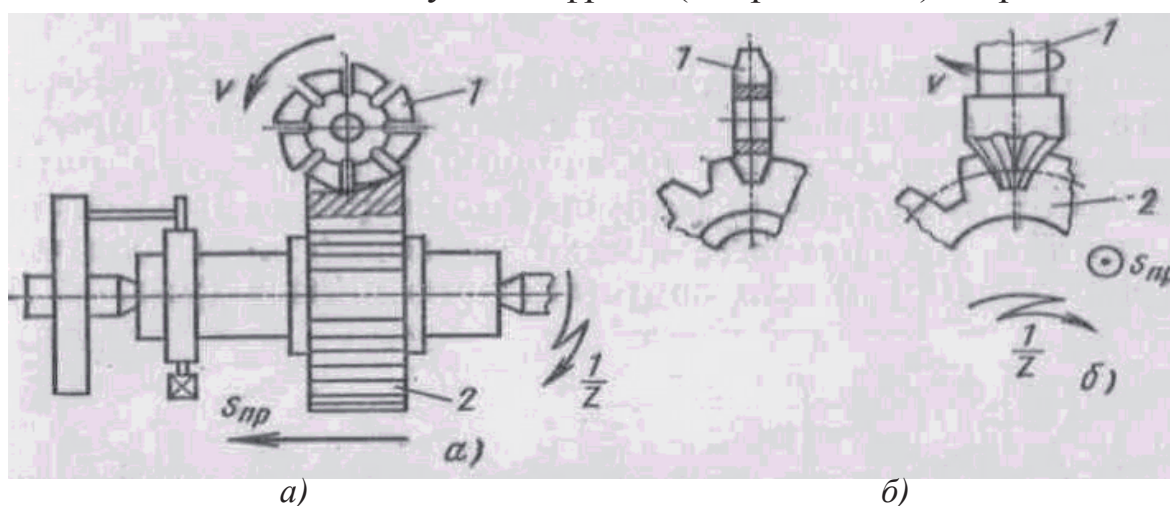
Нарезание зубчатых колес на универсально-фрезерных станках по методу копирования модульными фрезами: *а* – дисковой; *б* – пальцевой
